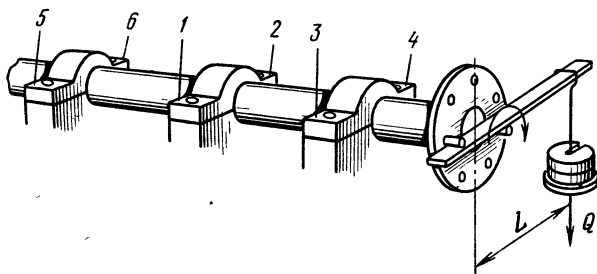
Порядок затягивания гаек подшипников и схема проверки вала на проворачивание
